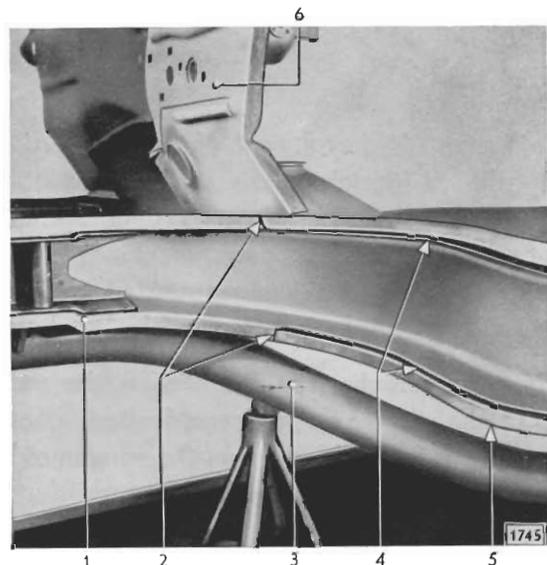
Linken Vorderrahmenlängsträger eingepaßt – rechten Längsträger in gleicher Weise einpassen
